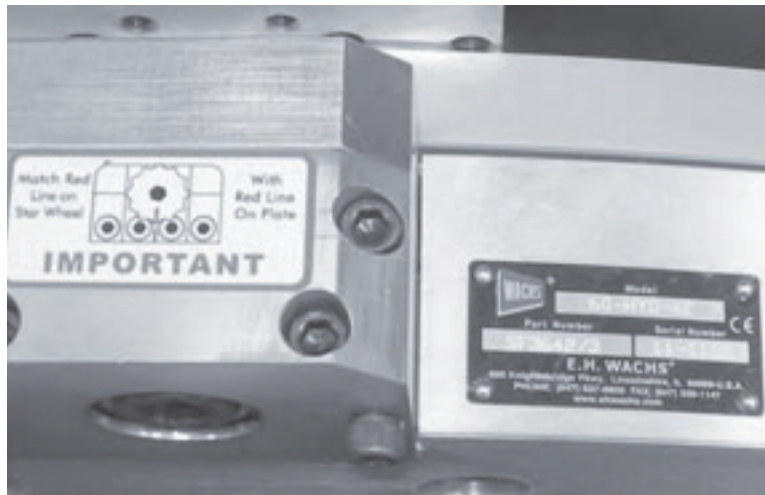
Наклейка с указанием внутреннего диаметра (размещается на неподвижной станции рядом с корпусом ведущей шестерни) указывает модель НПРА и включает серийный номер агрегата.
